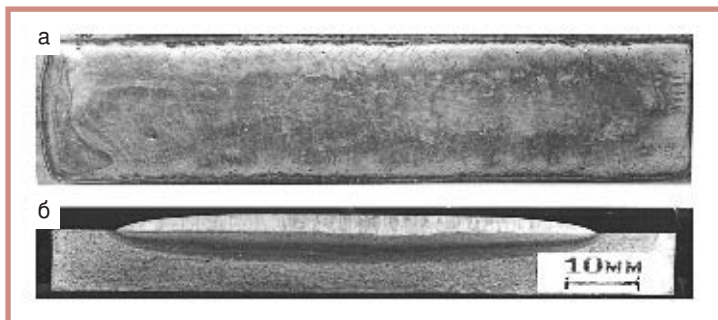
Внешний вид валика (а), наплавленного ЭШНЛ, и его макрошлиф (б)
